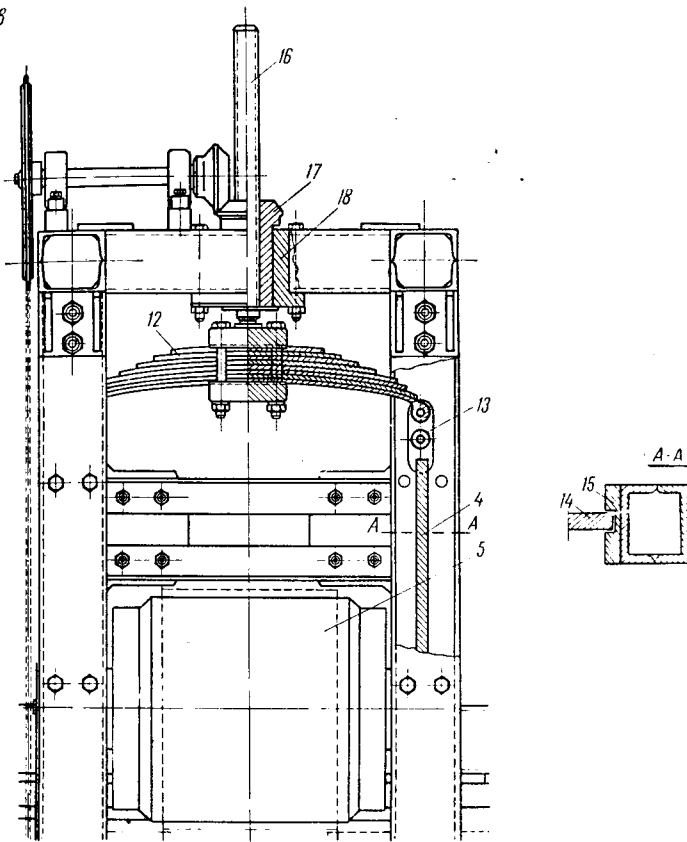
Наколочный станок ЦНИИС с механическим прижимом и листовой рессорой:
